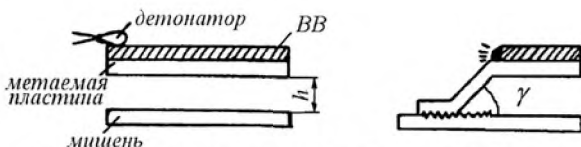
Схема сварки взрывом с параллельным расположением пластин
